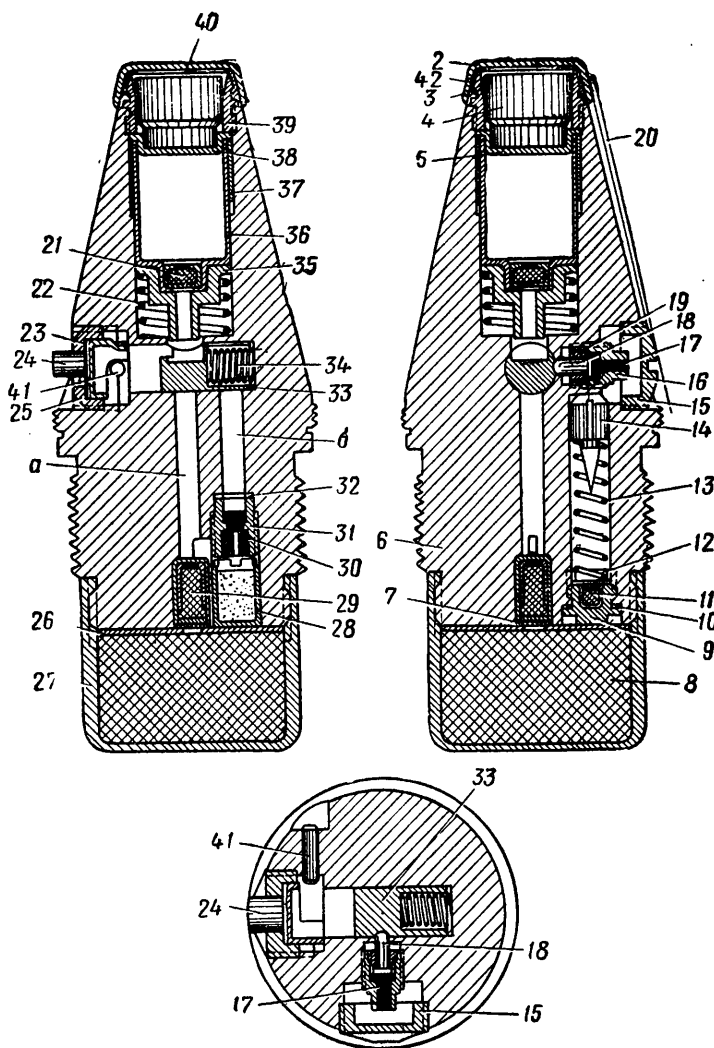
Положение деталей взрывателя до выстрела (колпак I свинчен):
